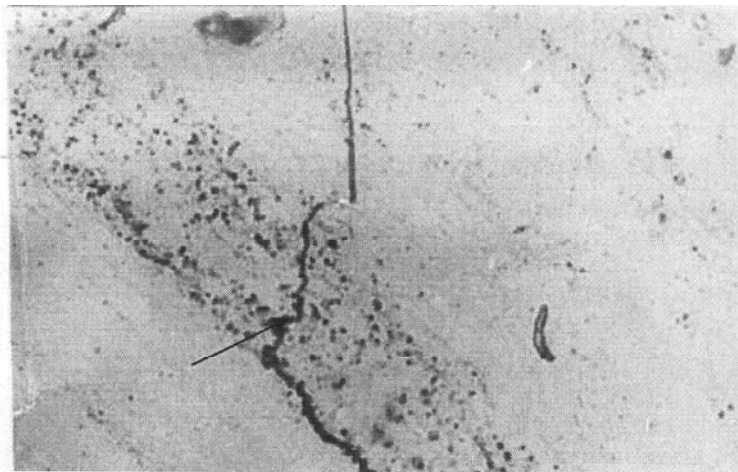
Усталостная микротрещина, образовавшаяся на участке сплавления ЗТВ (стрелка) сварного соединения паропровода острого пара из стали 12Х1МФ. х8000. Ресурс 200000 ч
